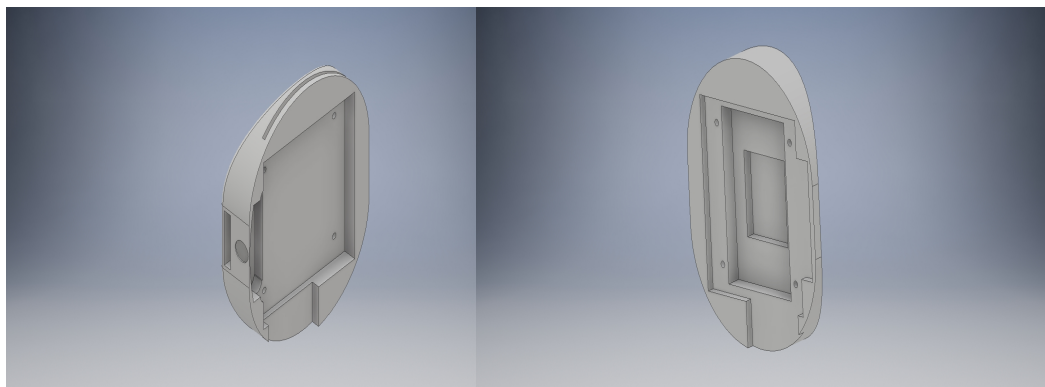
Izquierda: placa maestra final, derecha: PCB placa esclava final
